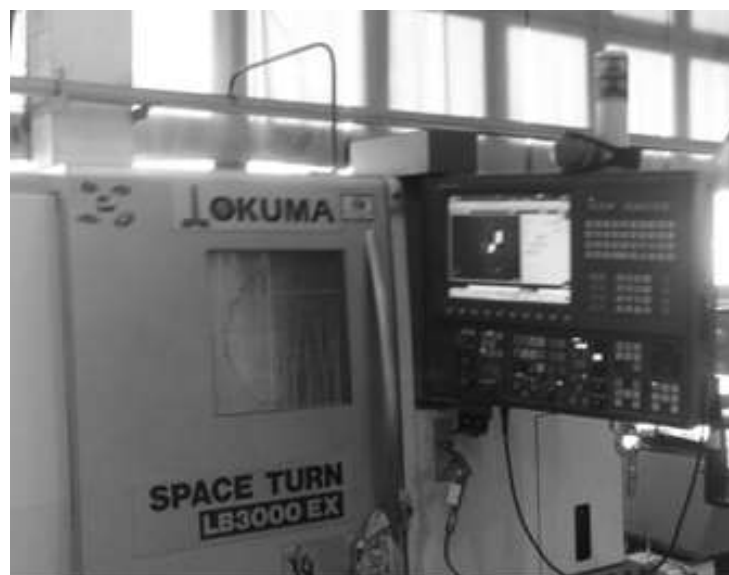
Верстат – Оброблювальний Центр SPACE TURN LB 3000EX
